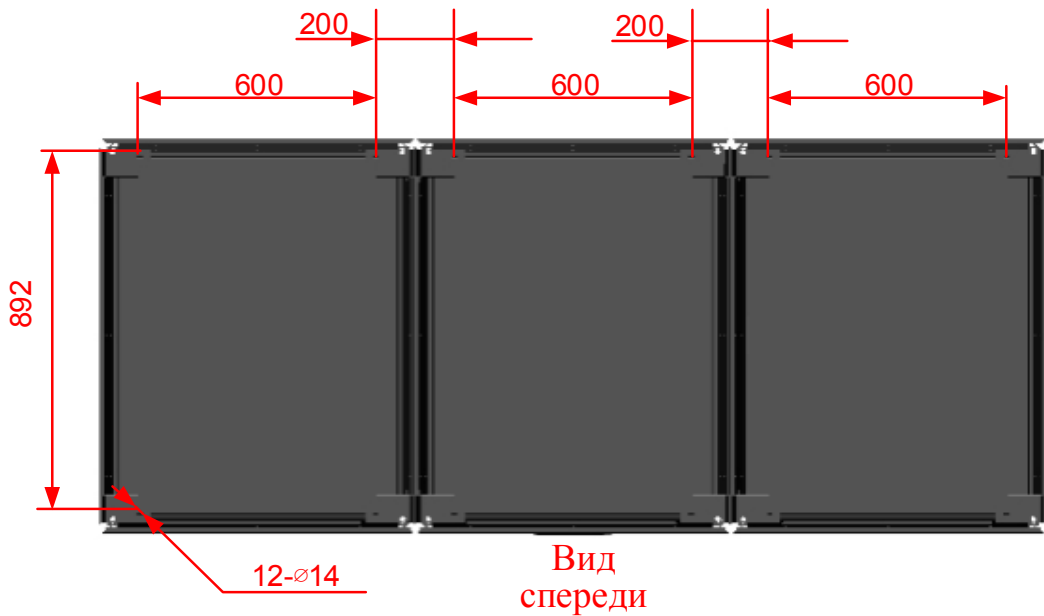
Размер установочного отверстия подставки MR331600 (ед. изм.: мм)
